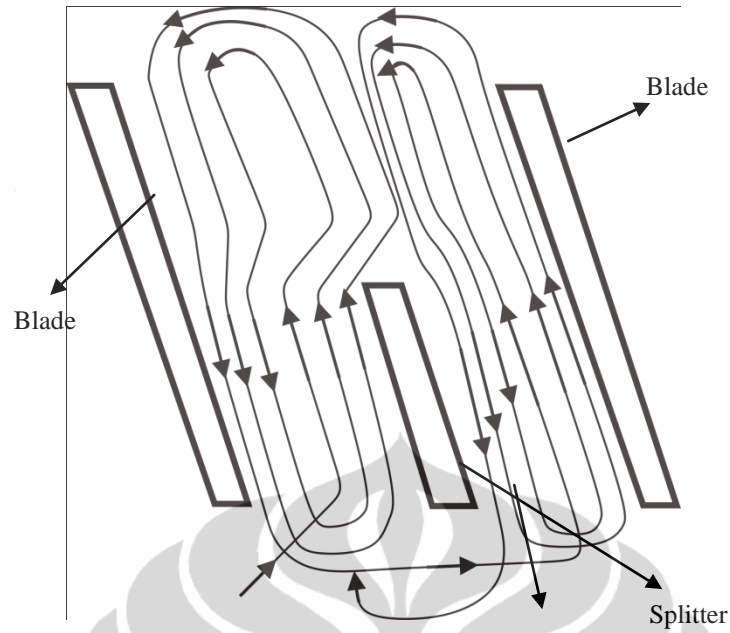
kemungkinan interference antara cutting tool dengan workpiece pada proses roughing impeller diameter 54 mm yang memiliki splitter
